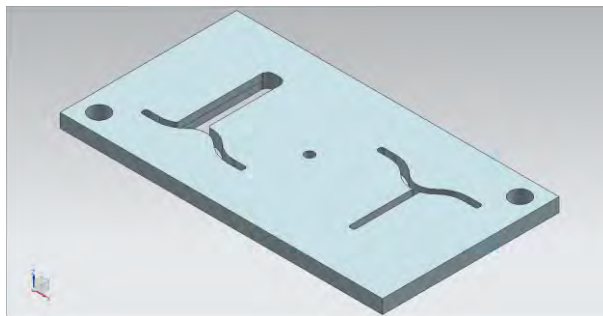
Modelo de diseño de la placa flotante molde 1.
